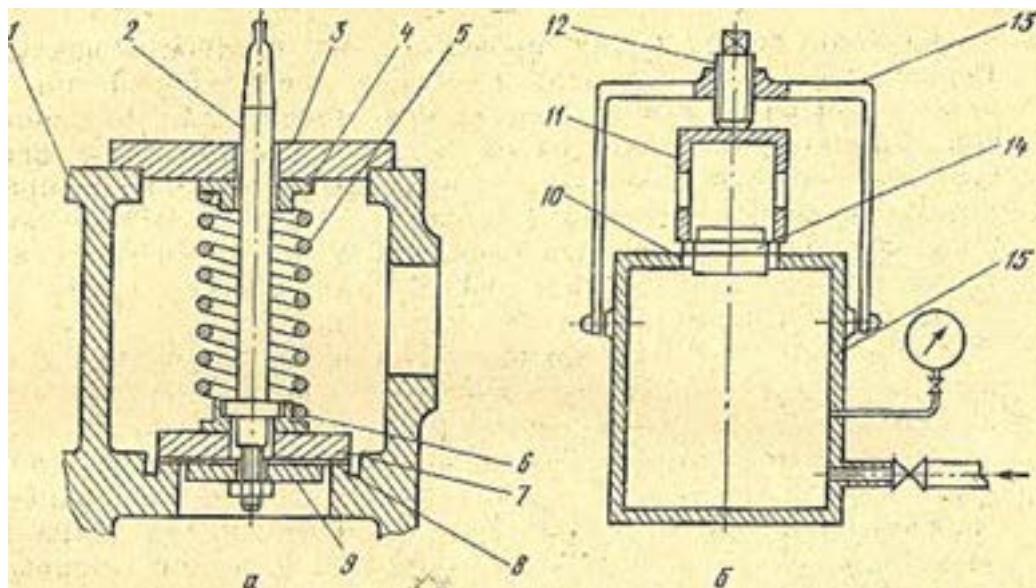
Приспособления для притирки посадочной поверхности в блоке цилиндров под клапан (а) и для проверки плотности клапана воздухом на утечку (б):
